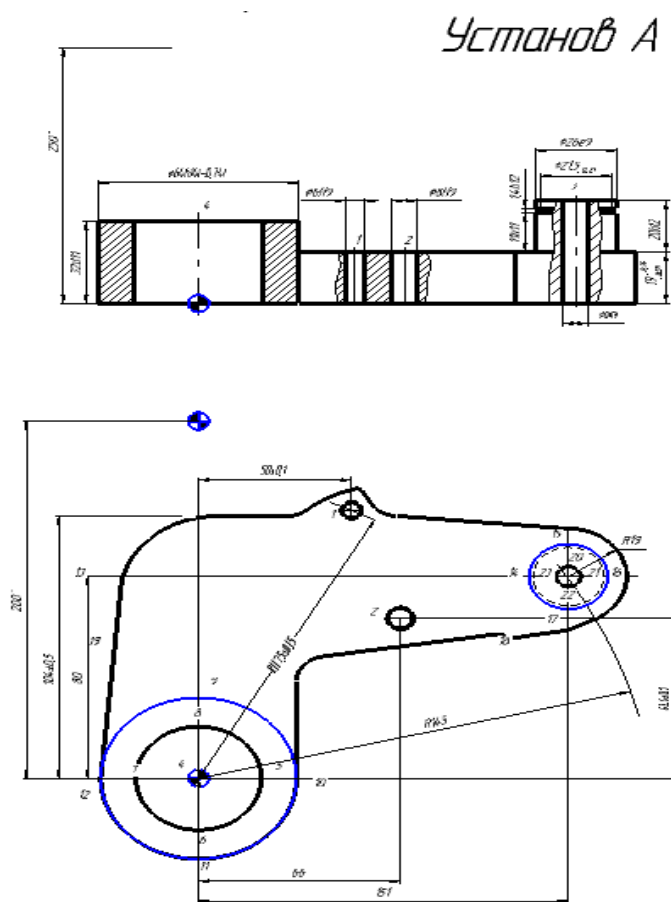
Схема базирования заготовки на операции 015 установ А
